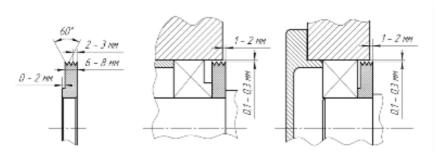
Конструкция мазеудерживающего кольца, подшипниковые узлы с использованием пластичного смазочного материала
